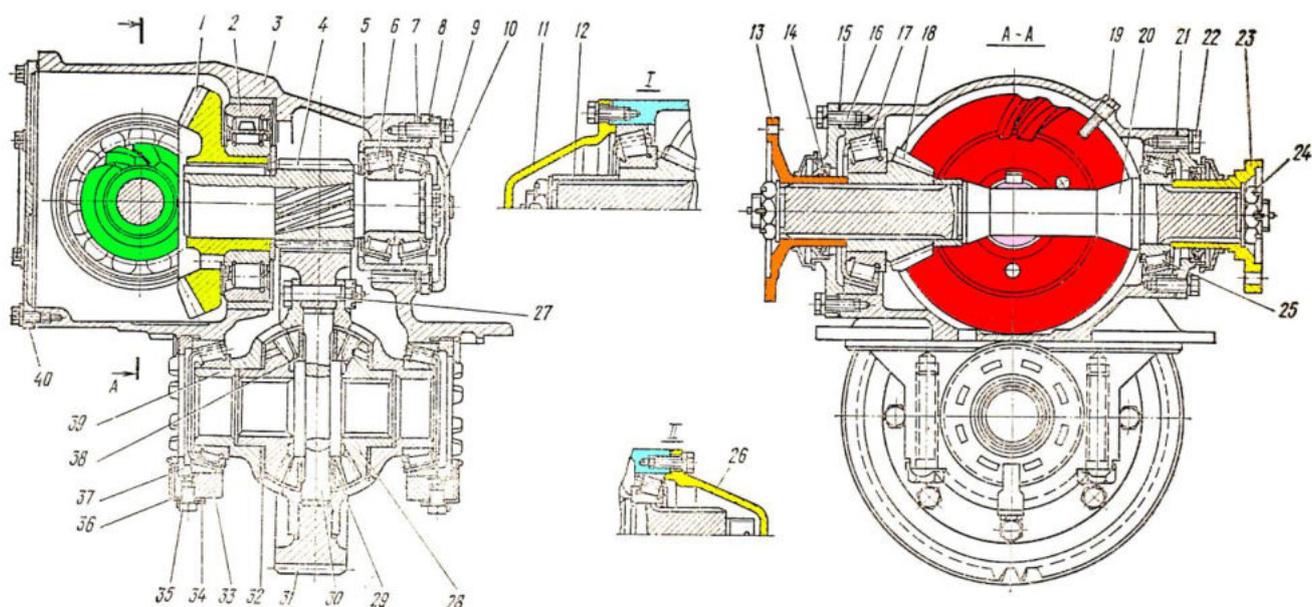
Редуктор главной передачи автомобилей семейства «Урал»:
